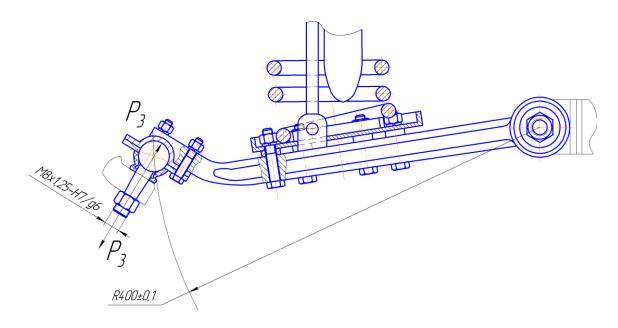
Расчётная схема нижней шаровой опоры
